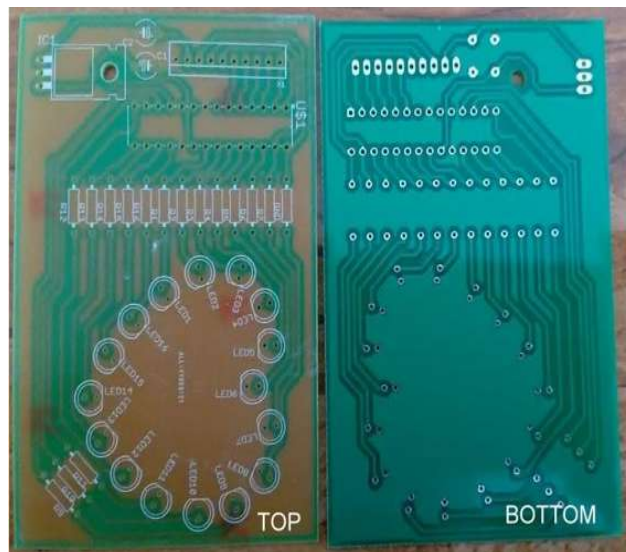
capas TOP y BOTTOM de una PCB de 1 capa de cobre [58]
